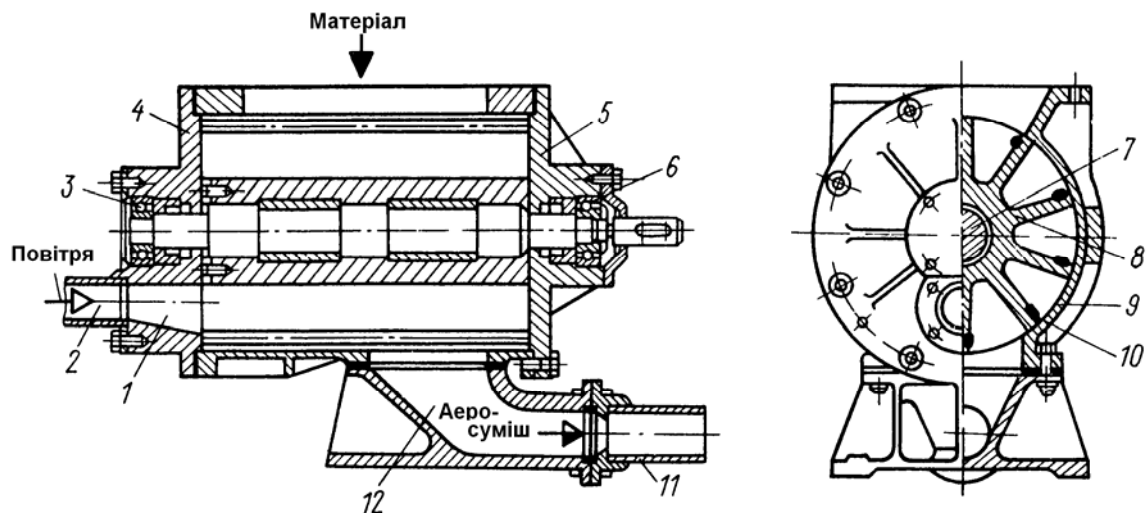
Шлюзовий живильник марки ХПШ: 1 – отвір; 2 – патрубок; 3,6 – підшипник; 4,5 – кришка; 7 – вал ротору; 8 – ротор; 9 – корпус; 10 – накладки; 11 – трубопровід.
